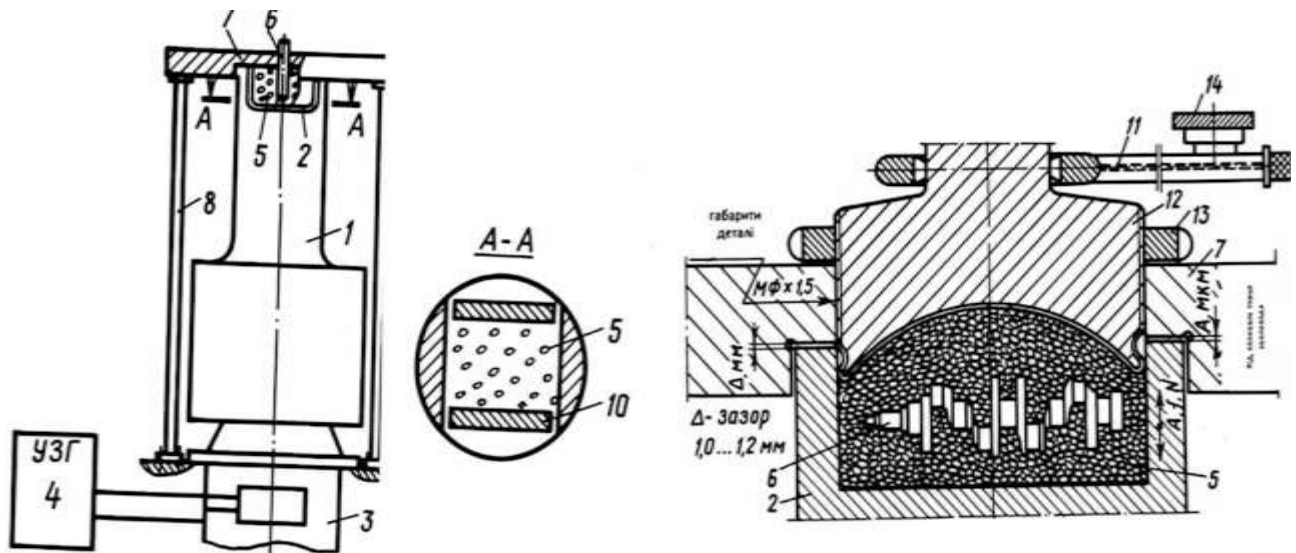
Пристрій для зміцнення деталей «колінчастий вал»: 1 – концентратор; 2 – асиметричне гніздо; 3 – магнітострикційний перетворювач; 4 – генератор; 5 – сталеві кульки; 6 – поверхня деталі; 7 – технологічний фланець; 8 – опорні стійки; 9 – станина; 10 – кришки; 11 – динамометричний ключ; 12 – пуансон; 13 – опора; 14 – прилад для вимірювання статичного зусилля
